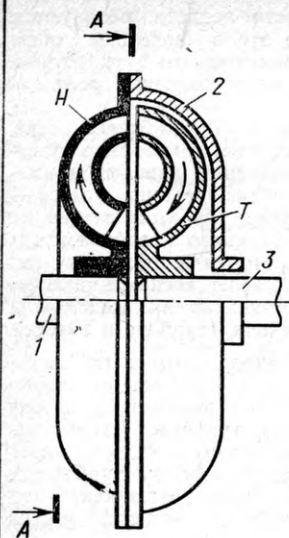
Конструктивная схема гидромукты: 1 — ведущий вал; 2 — кожух; 3 — ведомый вал
